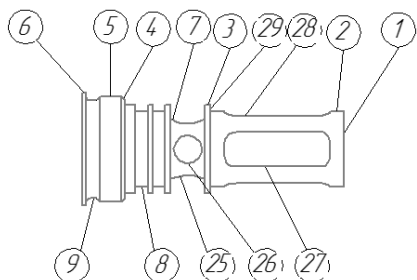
Условная нумерация поверхностей детали «Корпус фильтра»
